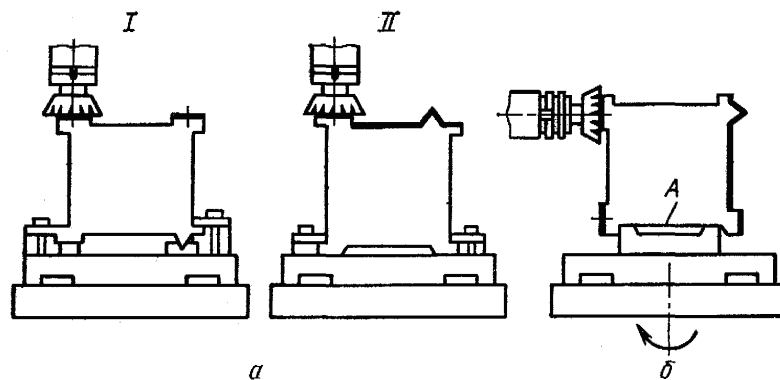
Схеми установки литої заготовки станини на палеті
